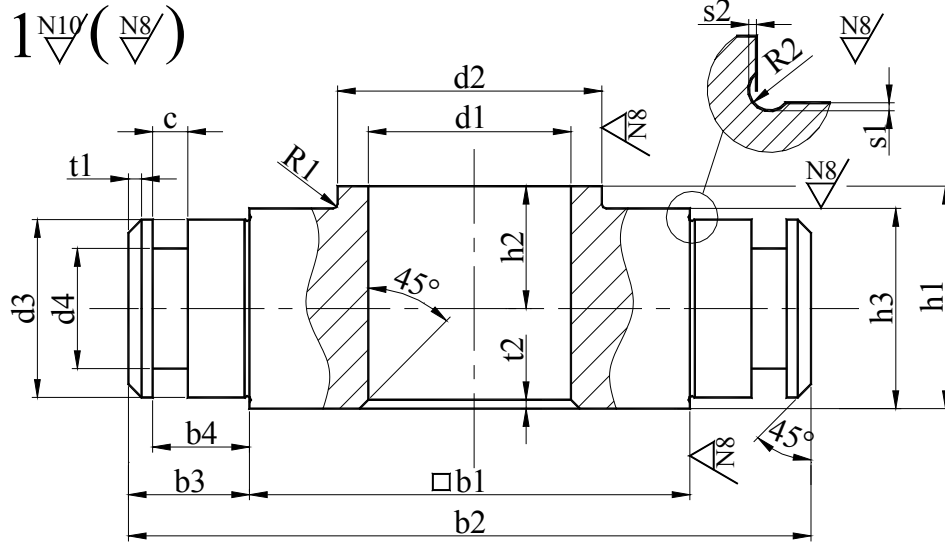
, Kalıpta ve Serbest dövme çiftli kancalar shaft işleme
